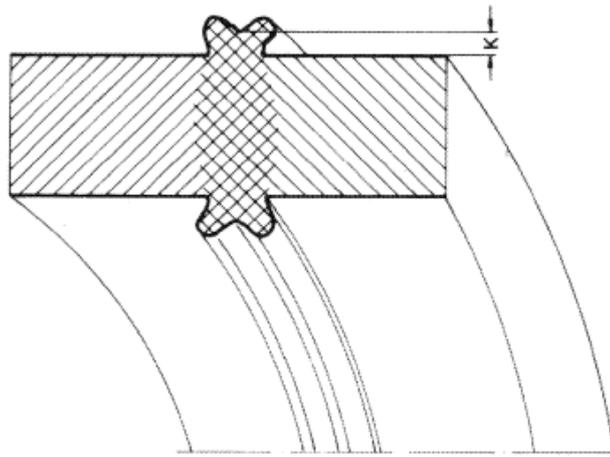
Вид грата при сварке нагретым инструментом.
